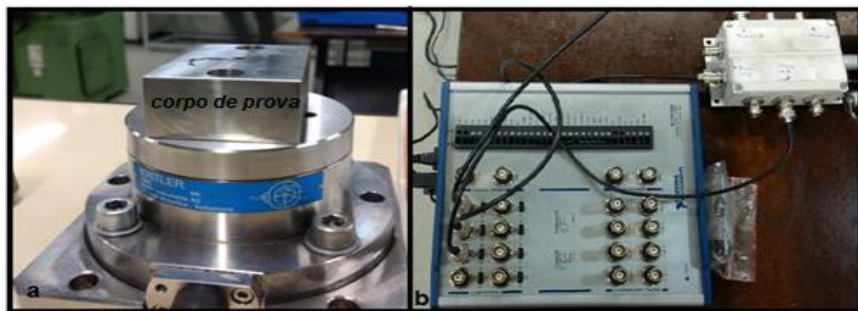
Montagem do corpo de prova no dinamômetro (a) e placa de aquisição de sinais(b).
